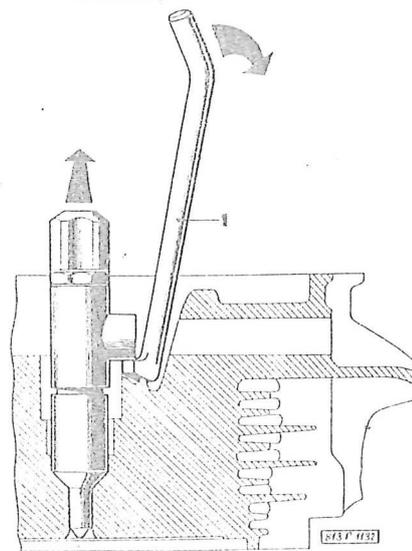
Ausbau des Einspritzventils aus dem Zylinderkopf
